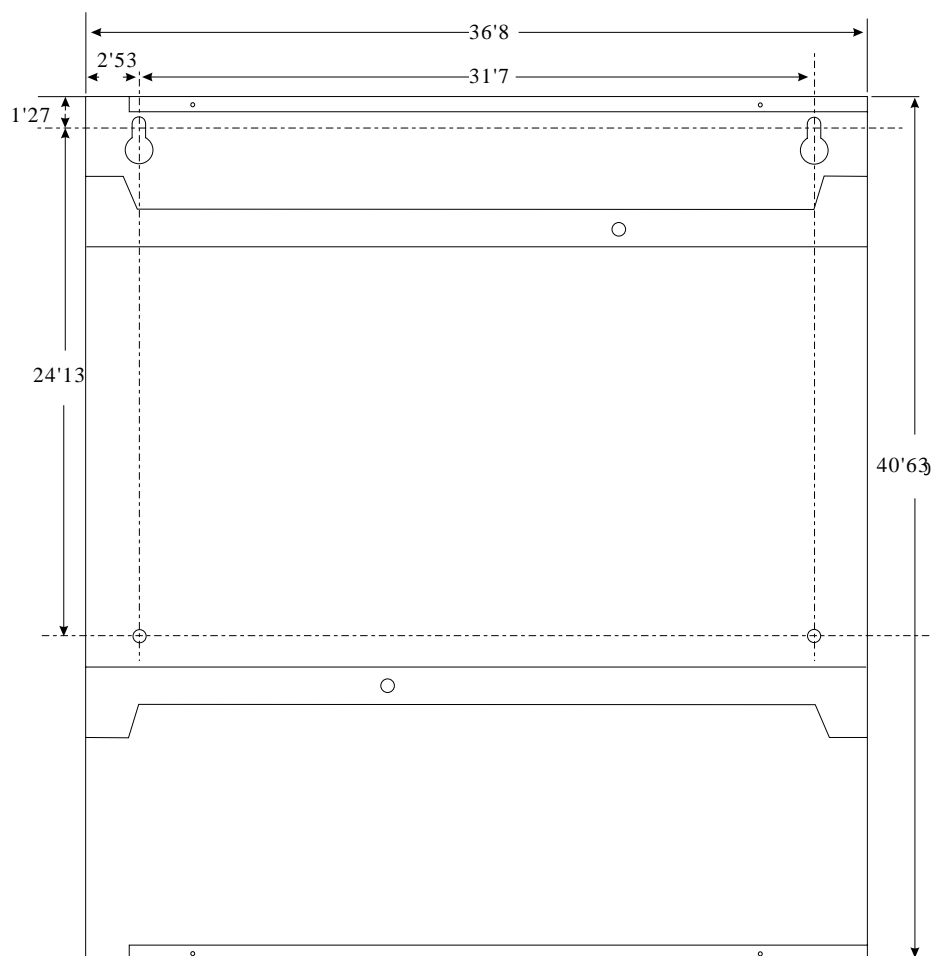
Dimensiones de la Cabina de la AFP-200 en cm.
